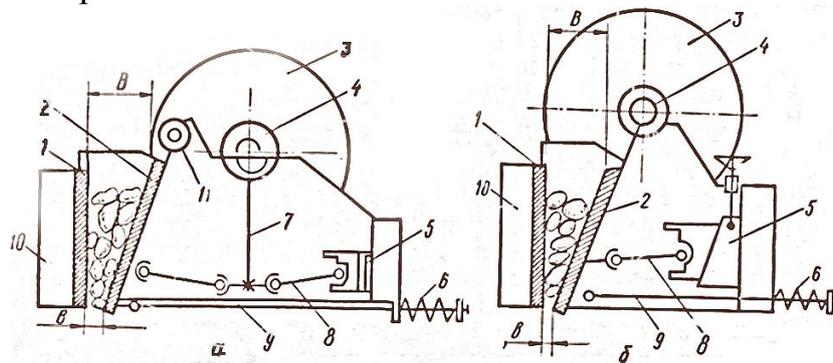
Конструктивные схемы щековых дробилок с простым (а) и сложным (б) качанием щеки: 1, 2 – неподвижная и подвижная щеки; 3 – маховик; 4 – эксцентриковый (главный) вал; 5 – гнездо упора распорных плит; 6 – пружины замыкающего механизма; 7 – шатун; 8 – распорная плита; 9 – тяга замыкающего механизма; 10 – станина; 11 – ось подвеса подвижной щеки; b – ширина разгрузочной щели (минимальная)
